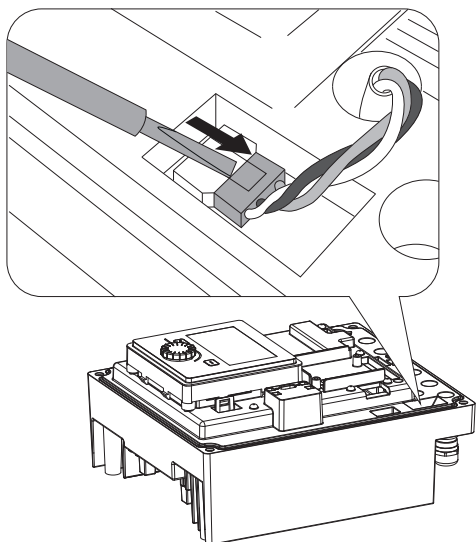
Soltar el cable de conexión del ventilador del módulo
